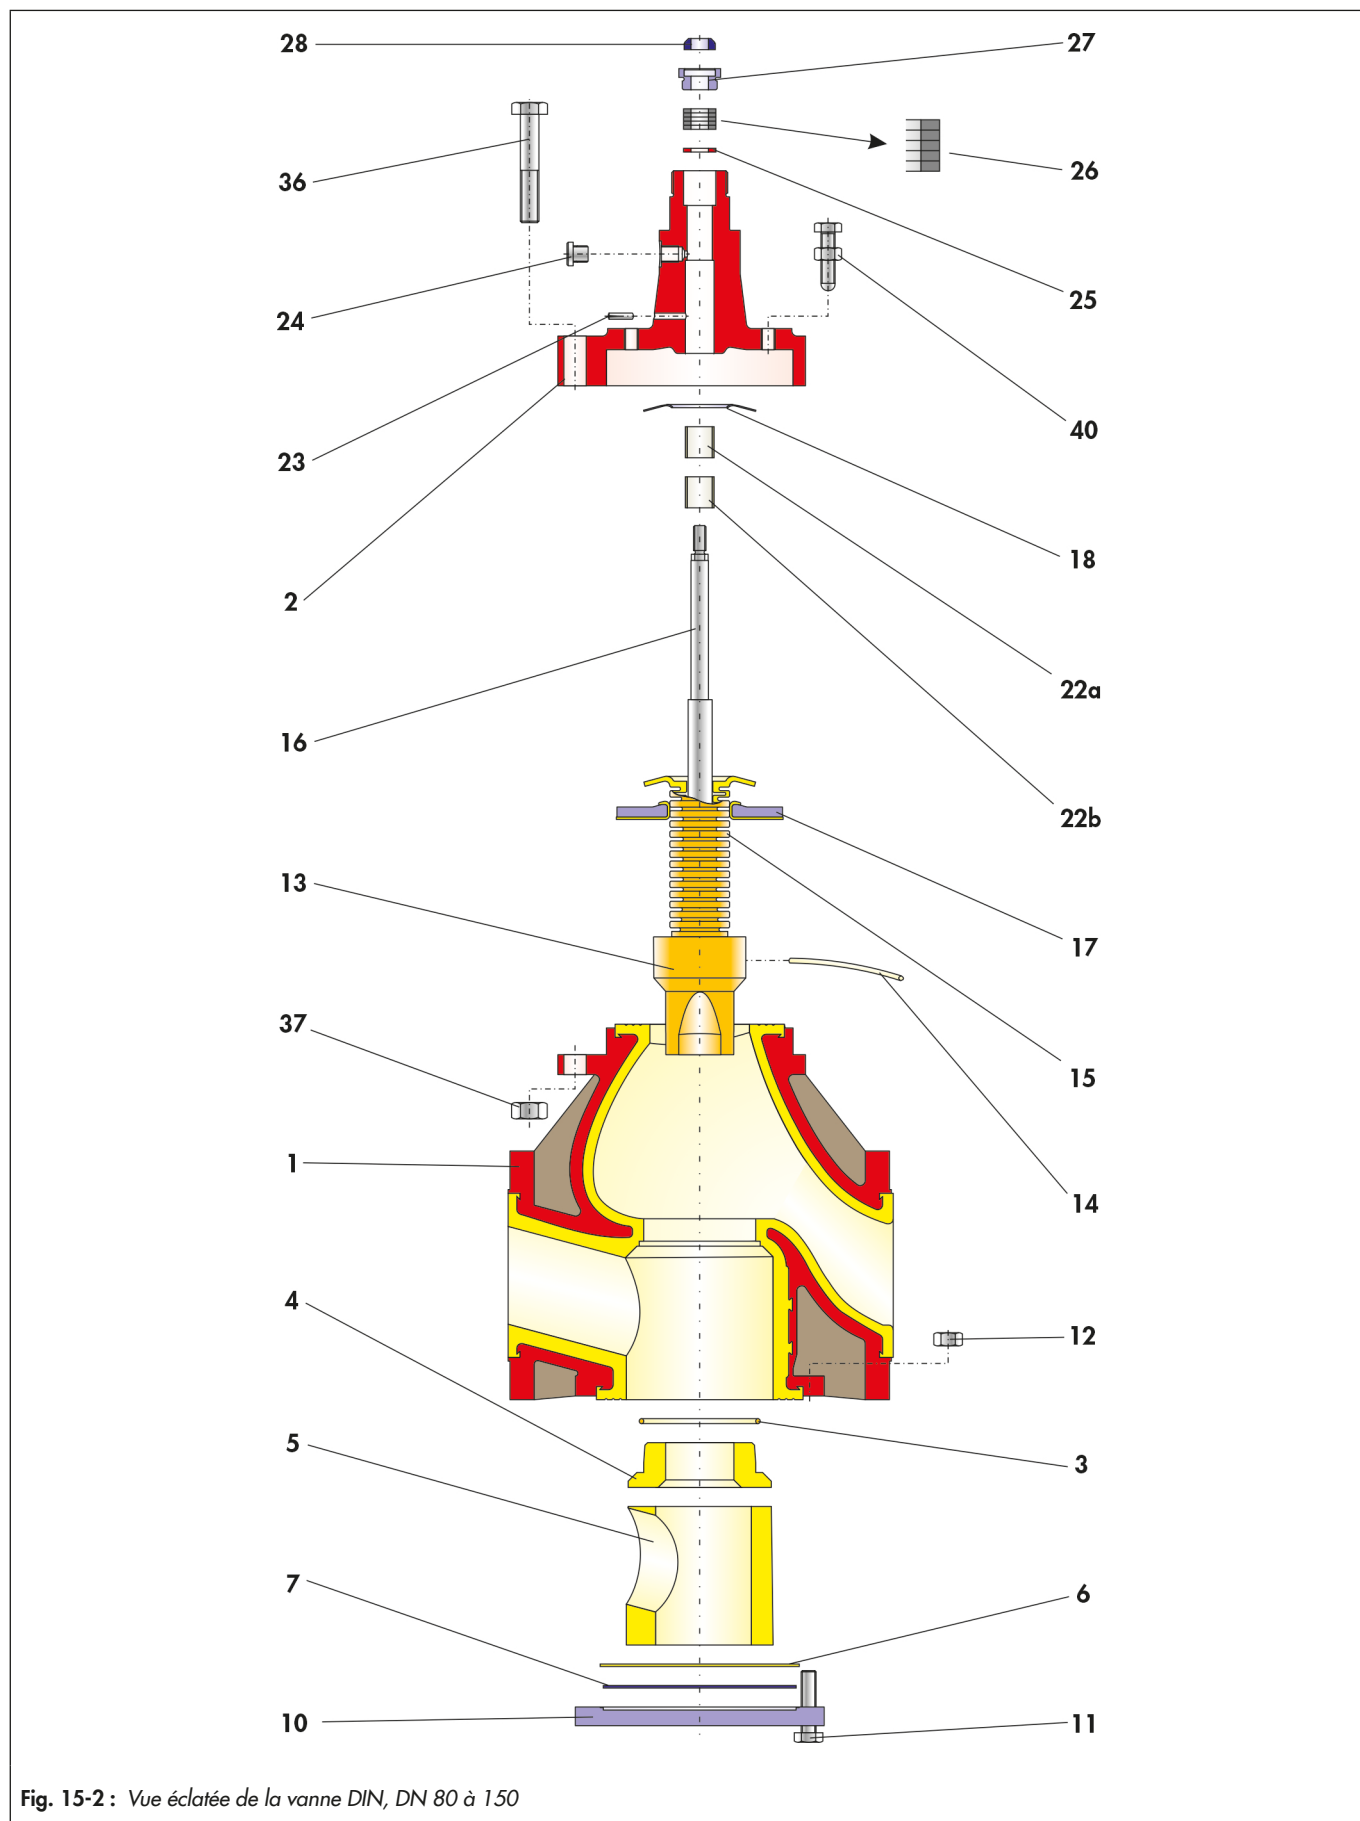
Vue éclatée de la vanne DIN, DN 80 à 150
